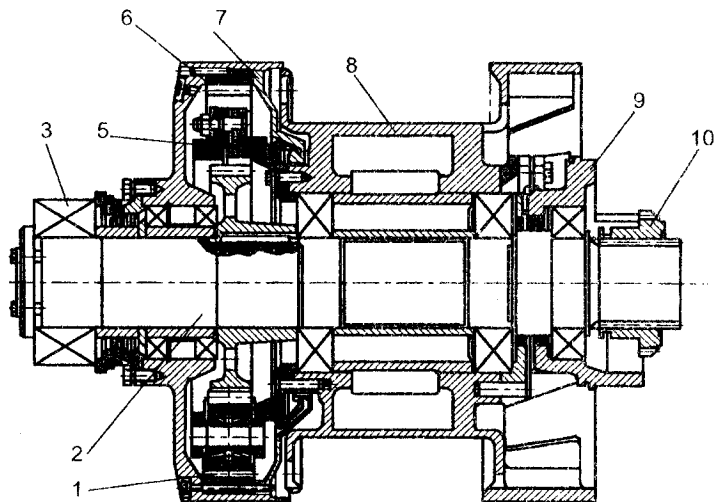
Лебідка верстата СКБ-5: 1 - шестірня-сателіт; 2 - вал; 3 - підшипник; 4 - сонячна шестірня; 5 - водило; 6 - прокладка; 7 - шків; 8 - барабан; 9 - стакан; 10 - зубчаста муфта
